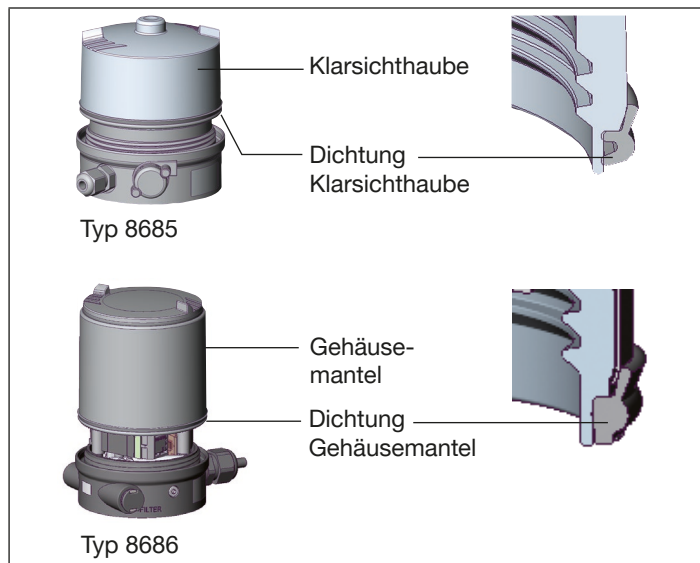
Position Dichtung Klarsichthaube / Gehäusemantel
